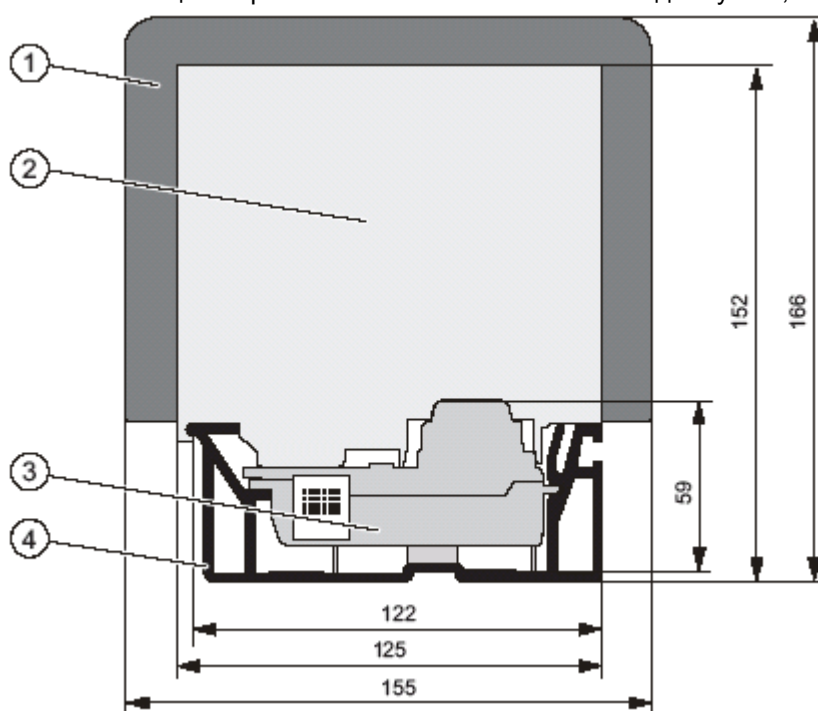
Габаритный чертеж 2000-миллиметровой профильной шины
